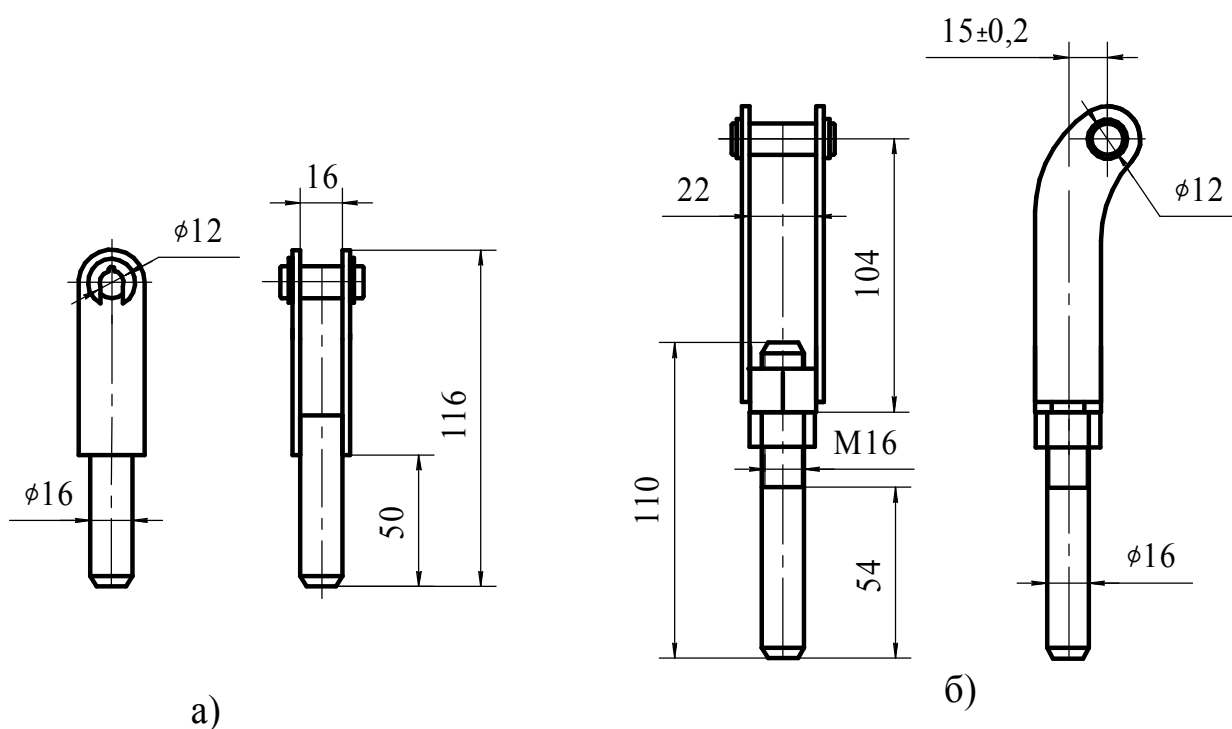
Вилки для соединения разъединителя с приводом:
